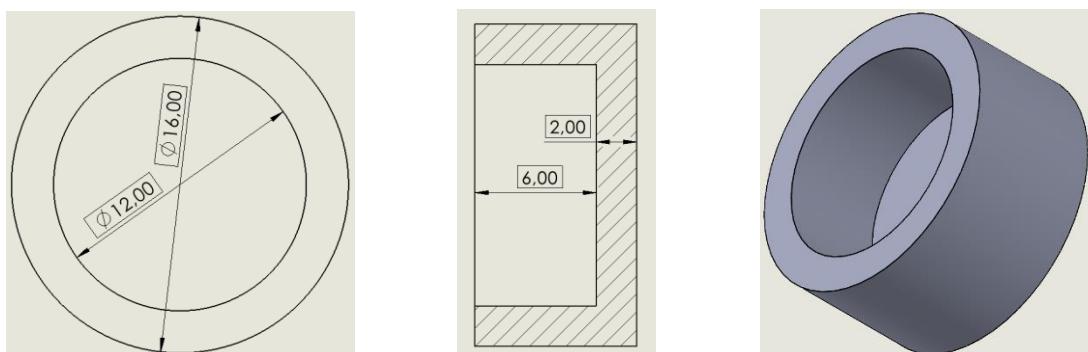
Geometría y dimensiones de la pieza 1, hecha en SolidWorks.
